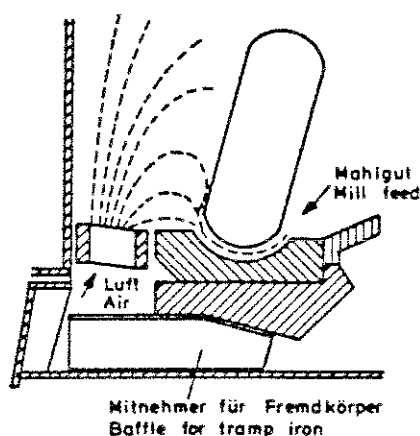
MPS-Mühle: Belüftung und Fremdkörperaustrag
